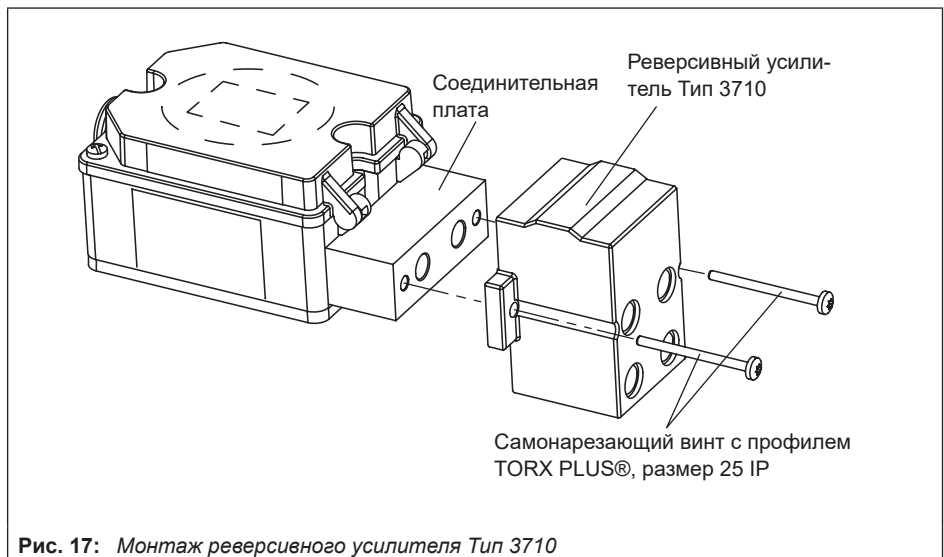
Монтаж реверсивного усилителя Тип 3710
